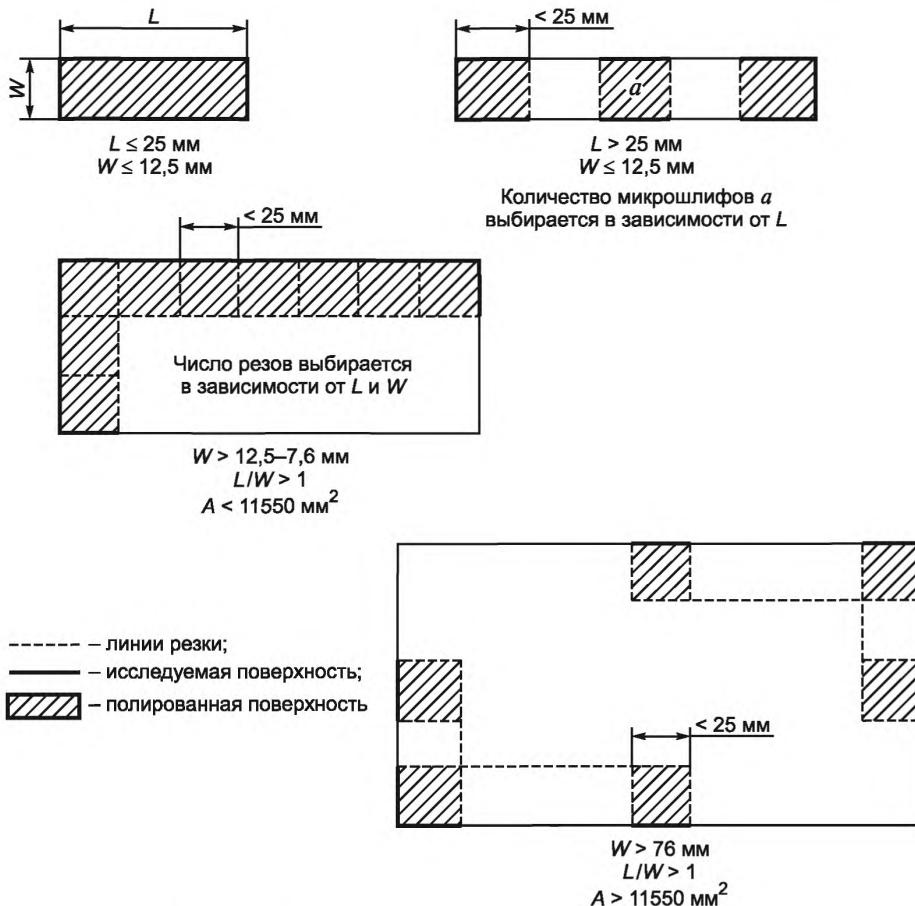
Типичные схемы отбора образцов для плоских и прямоугольных заготовок различного размера
